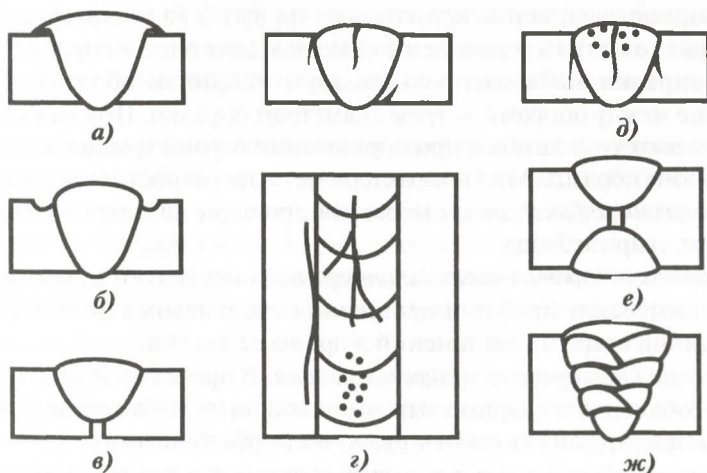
Виды дефектов в сварных соединениях
